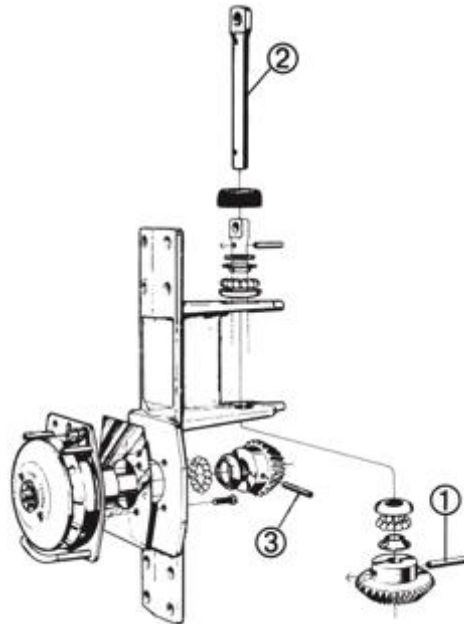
Despiece de enrollador de mayor de cabo sin fin. Fuente: Selden.
